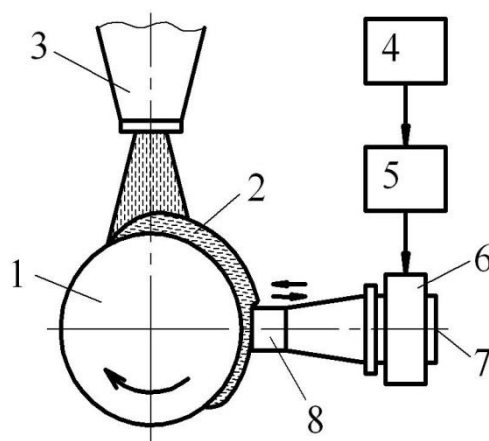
Схема активации металла детали перед напылением покрытия: 1 – обрабатываемая деталь; 2 – порошковое покрытие; 3 – плазматрон; 4 – ультразвуковой генератор; 5 – усилитель; 6 – обмотка возбуждения; 7 – вибратор; 8 – боек
